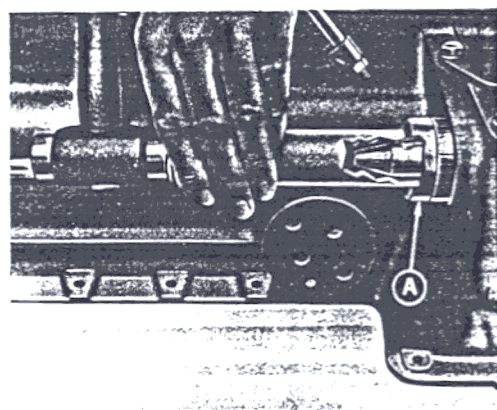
A-19D-01 — Montaje del retén de aceite del eje auxiliar
